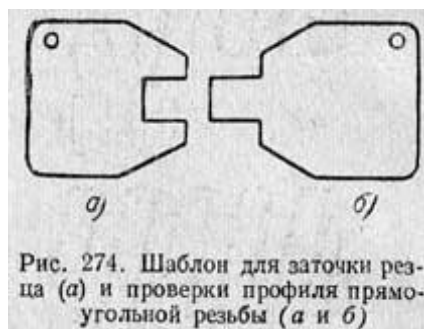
Шаблон для заточки резца (а) и проверки профиля прямоугольной резьбы (а и б)
